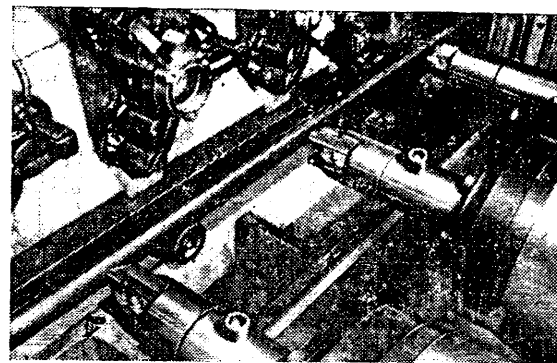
Резцовые вставки с непереключаемыми твердосплавными пластинами
